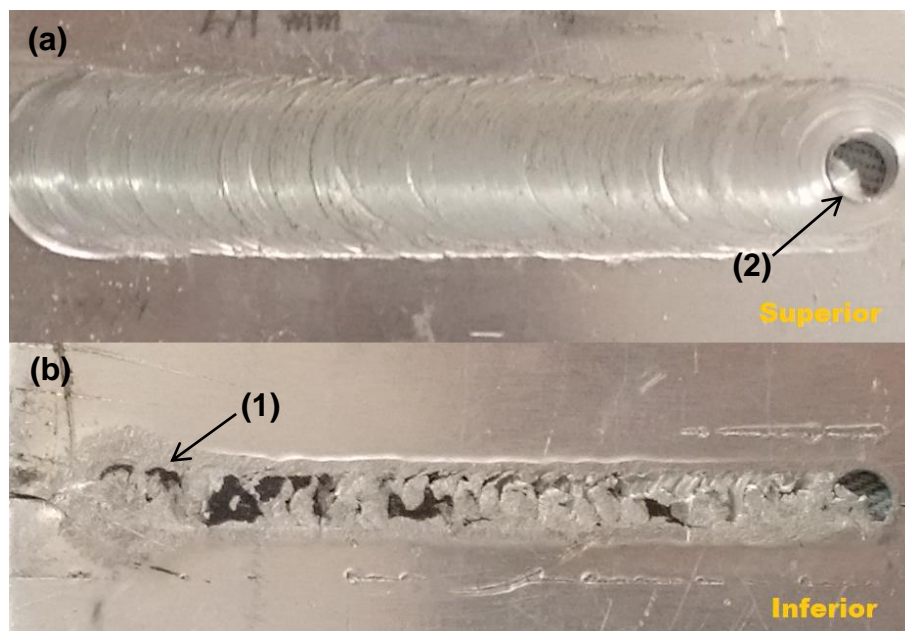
Ensaio para a determinação da altura do pino da ferramenta com um pino de 2,4 mm. Vistas (a) superior e (b) inferior da solda.
